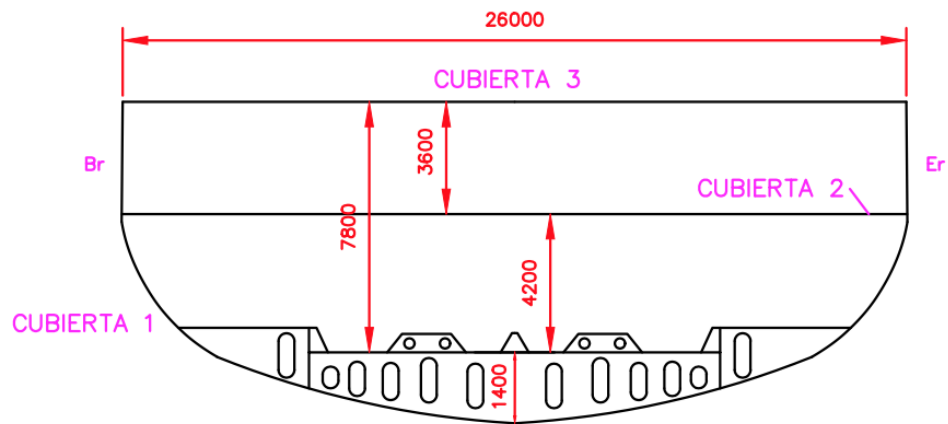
Sección transversal Sala Máquinas. Elaboración propia AutoCad.
